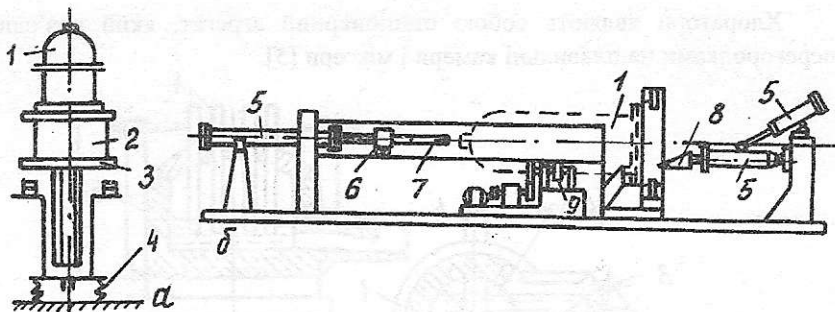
Схеми установки для витрупування (а) і гідралічного преса для підрізування гарнісажної корки і виштовхування блоків губки (б): 1-реторта з блоком; 2-корзина; 3-підійомно-падаючий стіл; 5-гідроциліндри; 6-каретка; 7-штемпель; 8-ножі; 9-приводні ролики
